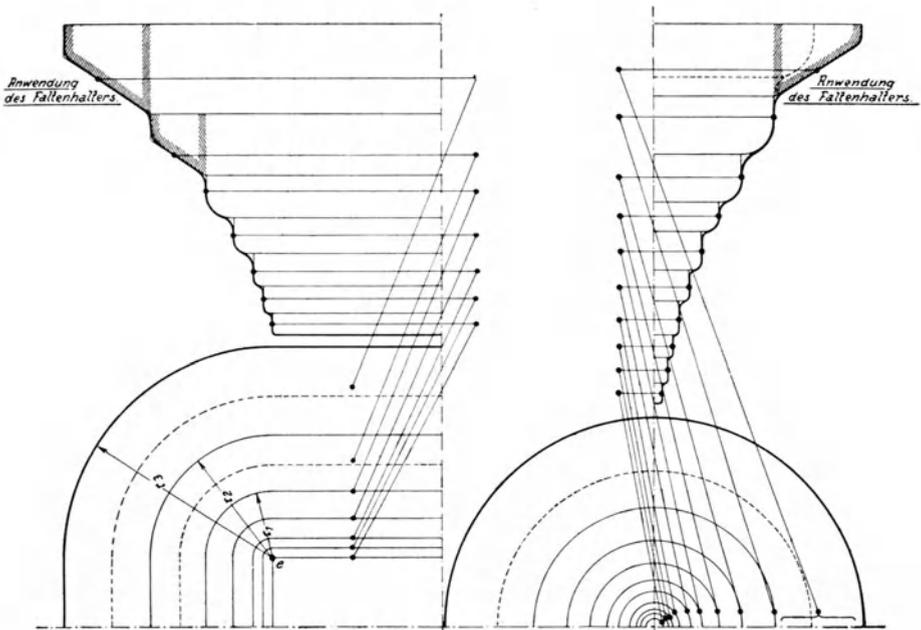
Ziehstufenbild mit Kantenabrundungen für runde und eckige Hohlkörper.
